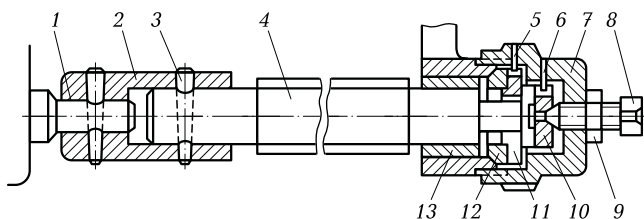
Сборочная единица «ходовой винт — гайка»:
